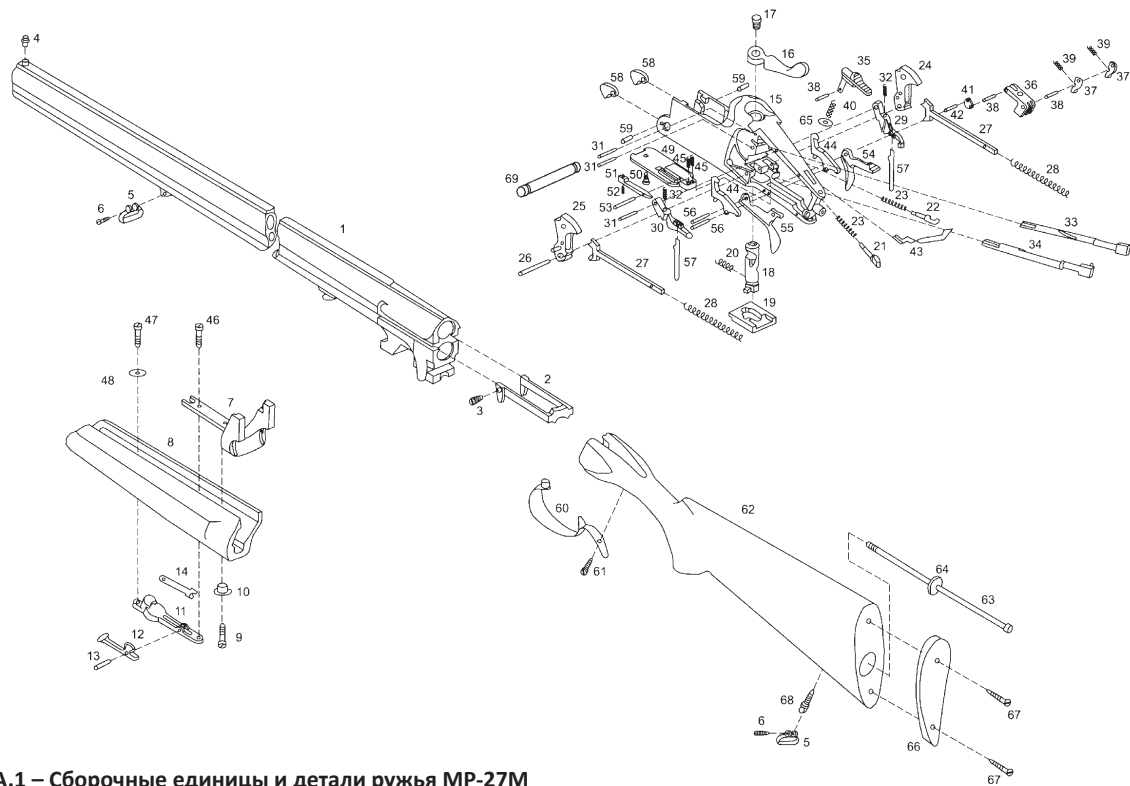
Сборочные единицы и детали ружья МР-27М
